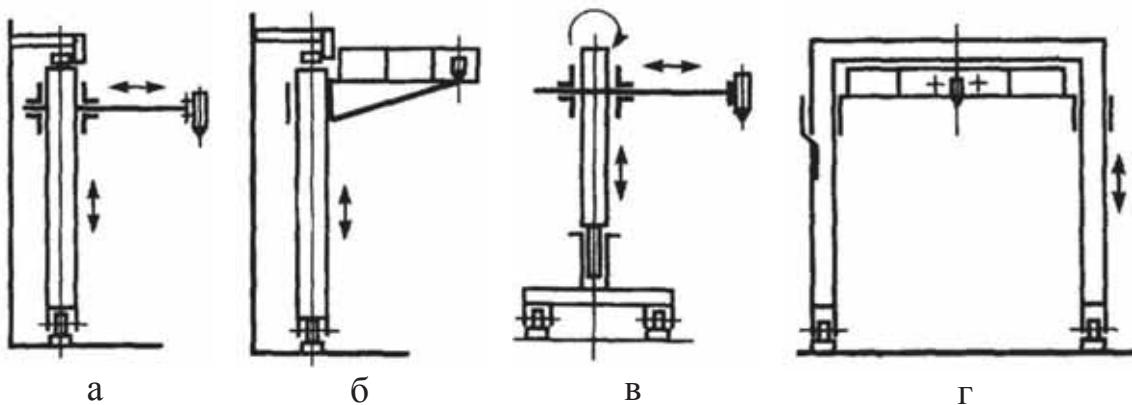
Типы опор для сварочных автоматов: а, б – велосипедные; в – глагольная; г – порталная
